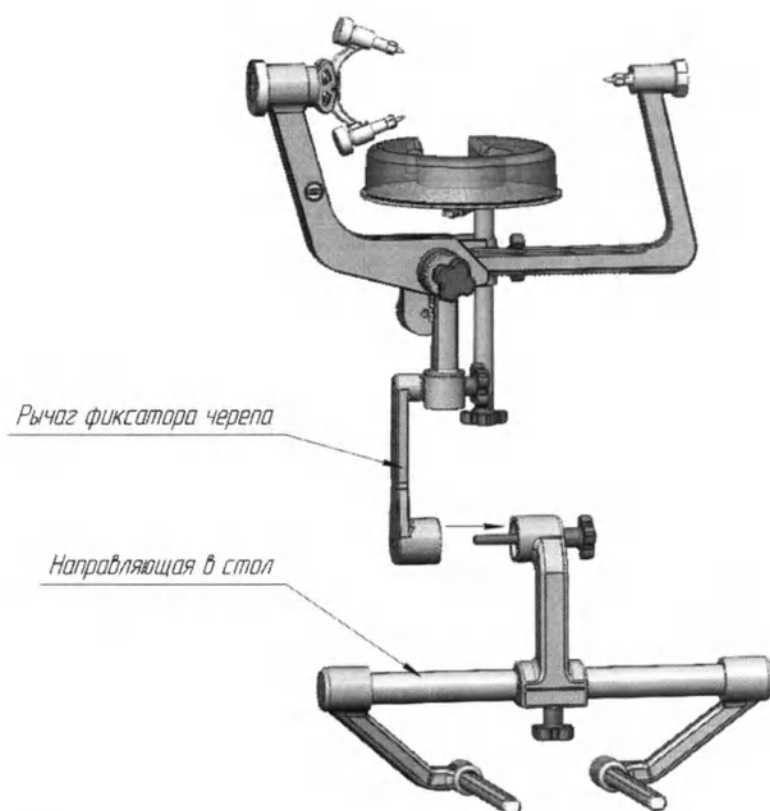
Крепление рычага фиксатора черепа к направляющей в стол
